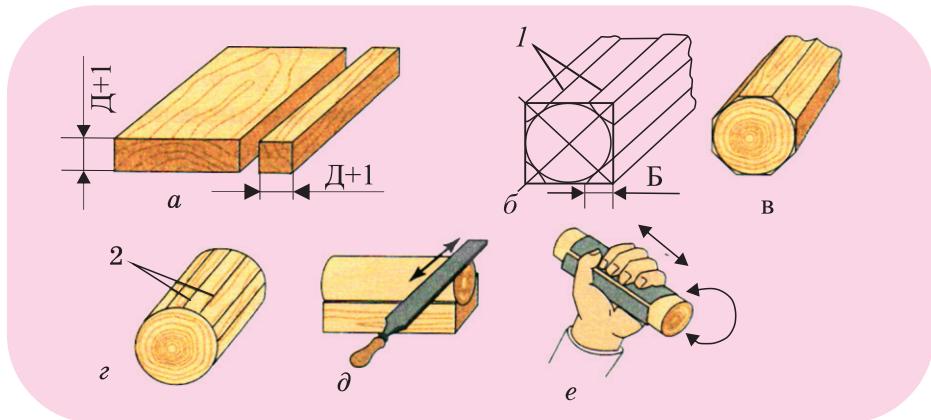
Последовательность изготовления детали цилиндрической формы ручным инструментом:
